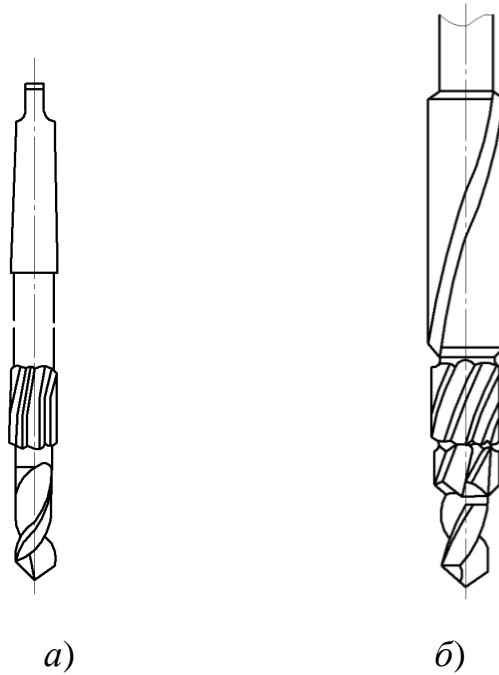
Комбінований інструмент для оброблення отворів:
